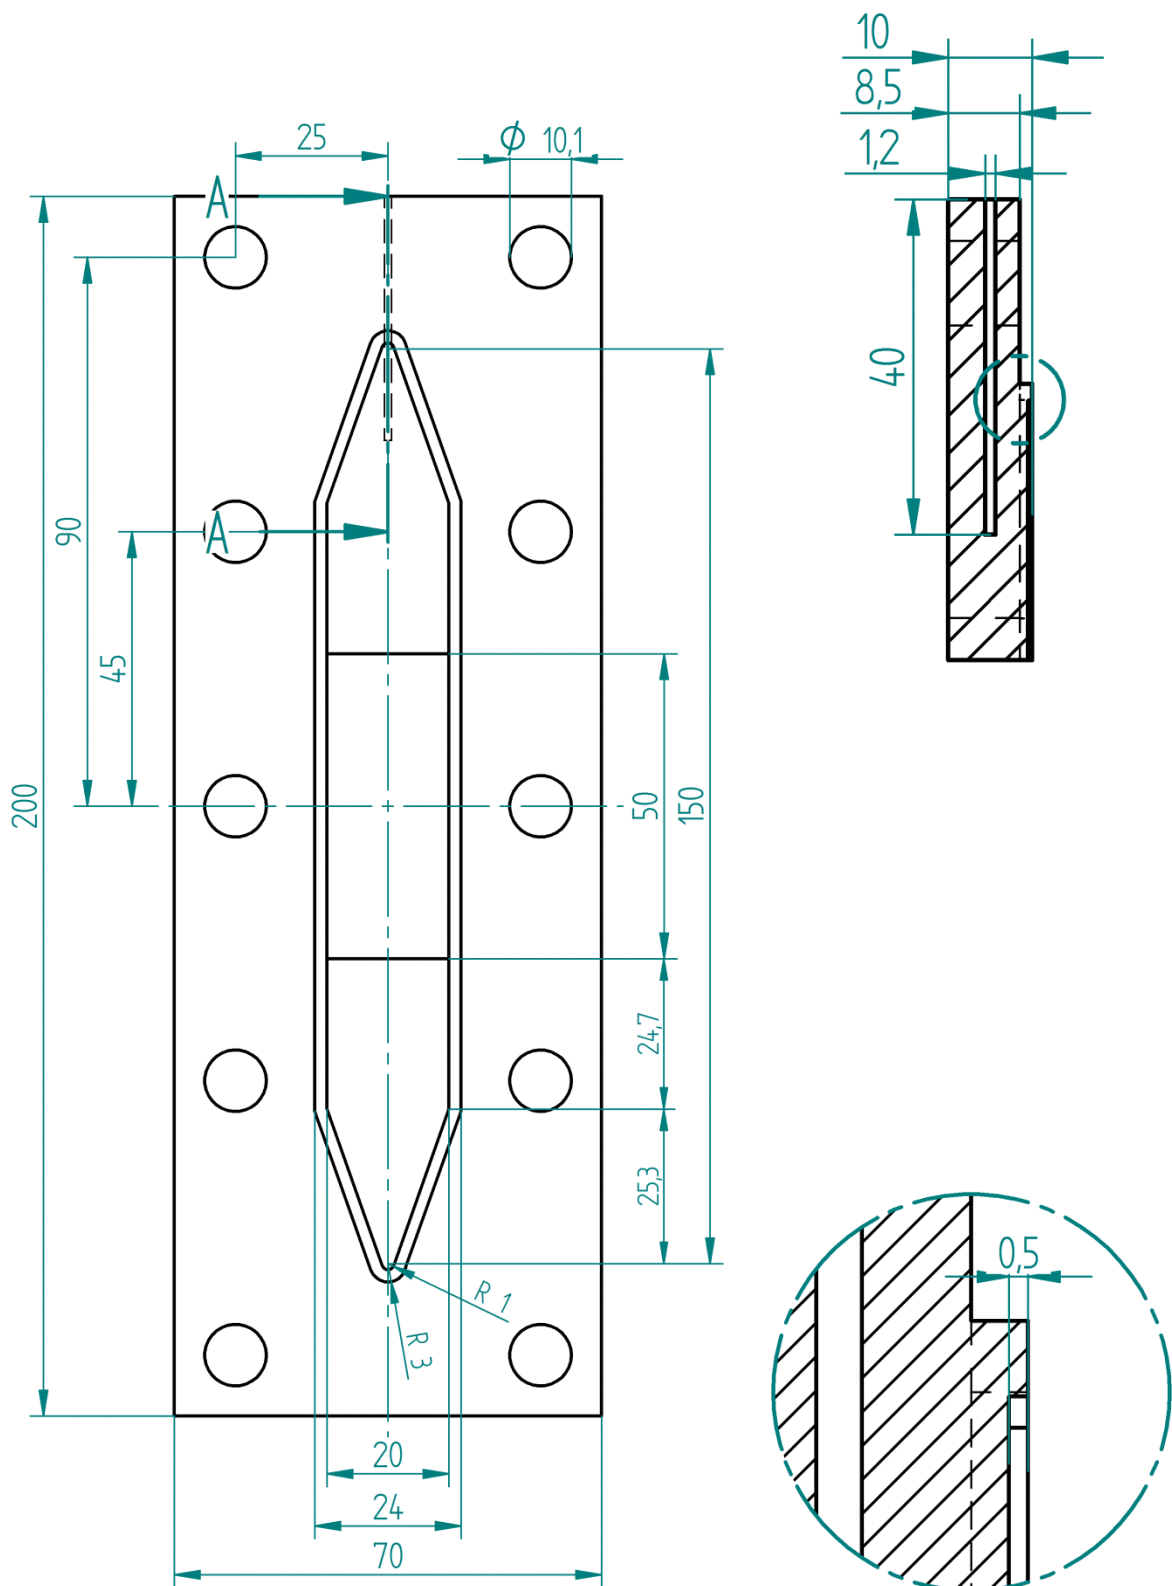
Konstruktionszeichnung der Bodenplatte. Dargestellt sind die Draufsicht (links), der Schnitt A-A (rechts oben) und eine Vergrößerung innerhalb des Schnittes (rechts unten). Alle Abmessungen in Millimeter.
